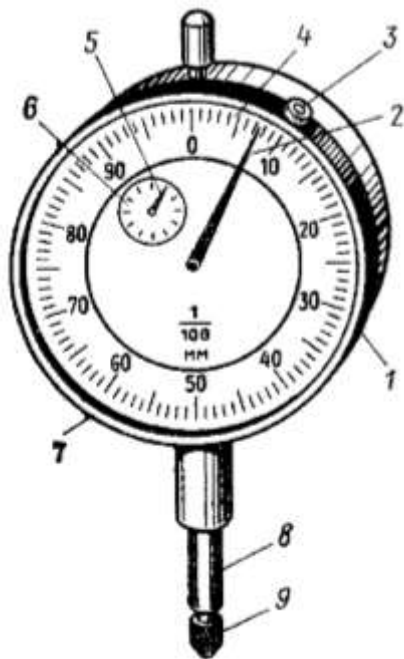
Індикатор годинникового типу: 1 – корпус; 2 – стрілка; 3 – стопор; 4 – вимірювальна шкала; 5 – стрілка покажчика; 6 – мала шкала; 7 – обідок для устанавлення нуля; 8 – вимірювальний стрижень; 9 – наконечник
